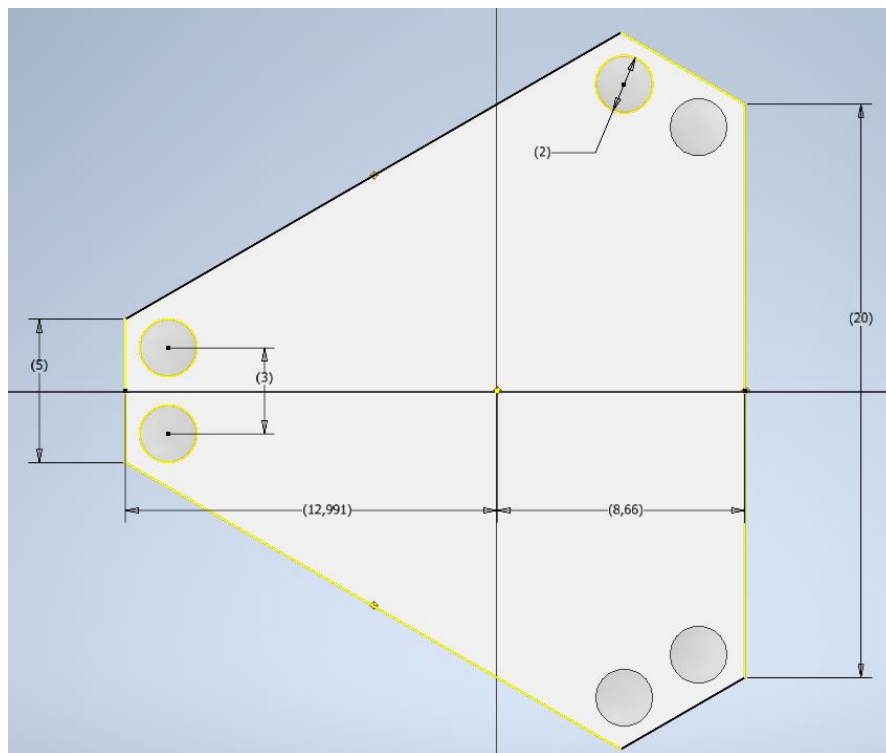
Vista de alzado de la plataforma inferior fija o base
